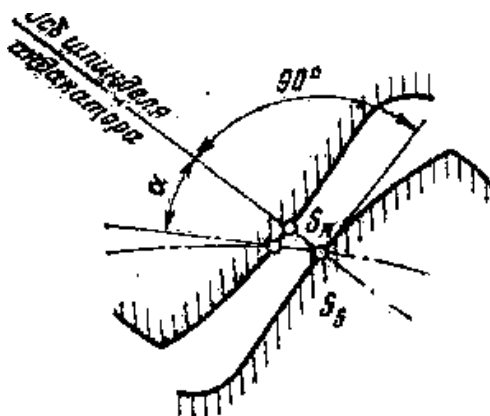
Схема измерения бокового зазора между зубьями зубчатых колес с помощью индикатора
